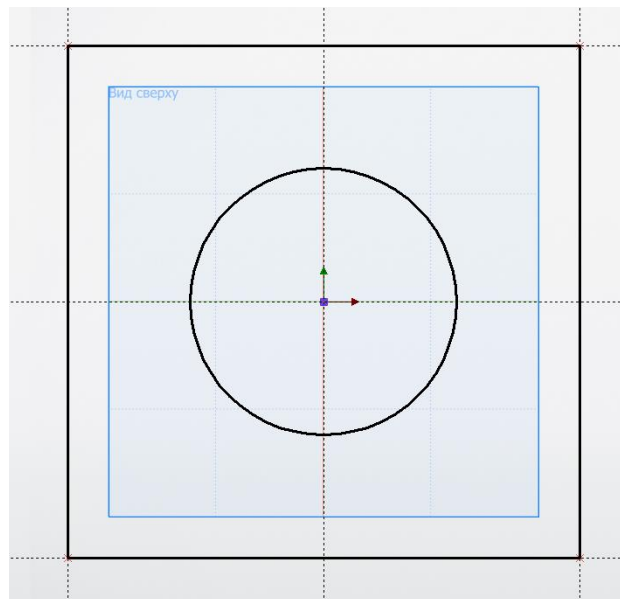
Эскиз нижней части верхней пластины опорно-поворотного устройства
